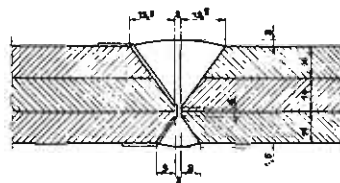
Coupe des cordons de soudure de la partie au droit des cornières.
